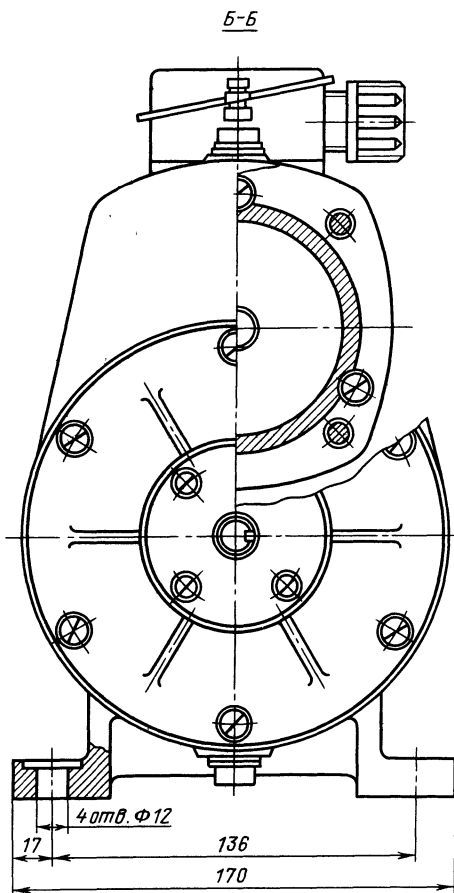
Чертеж общего вида «Мотор-редуктор»
